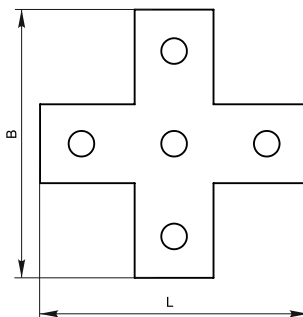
Пластина соединительная X-образная для STRUT-профиля
